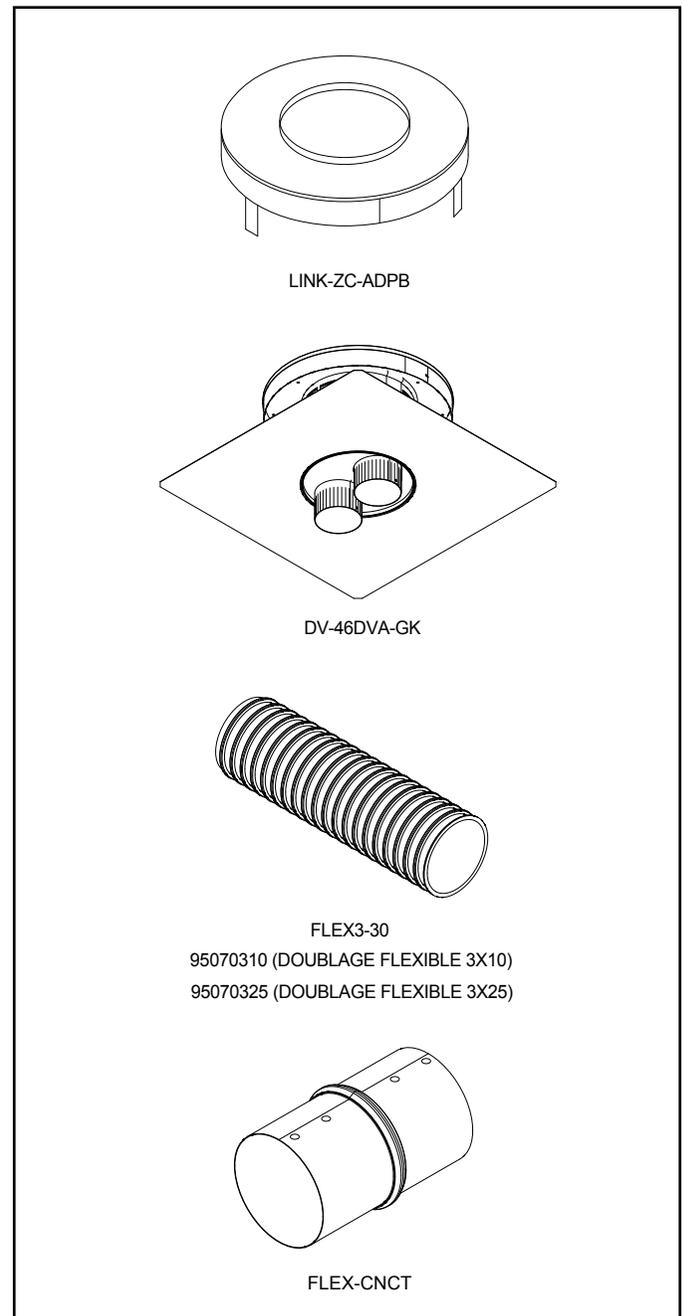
Ensembles d'accessoires de doublage de conduit flexible d'évacuation directe
